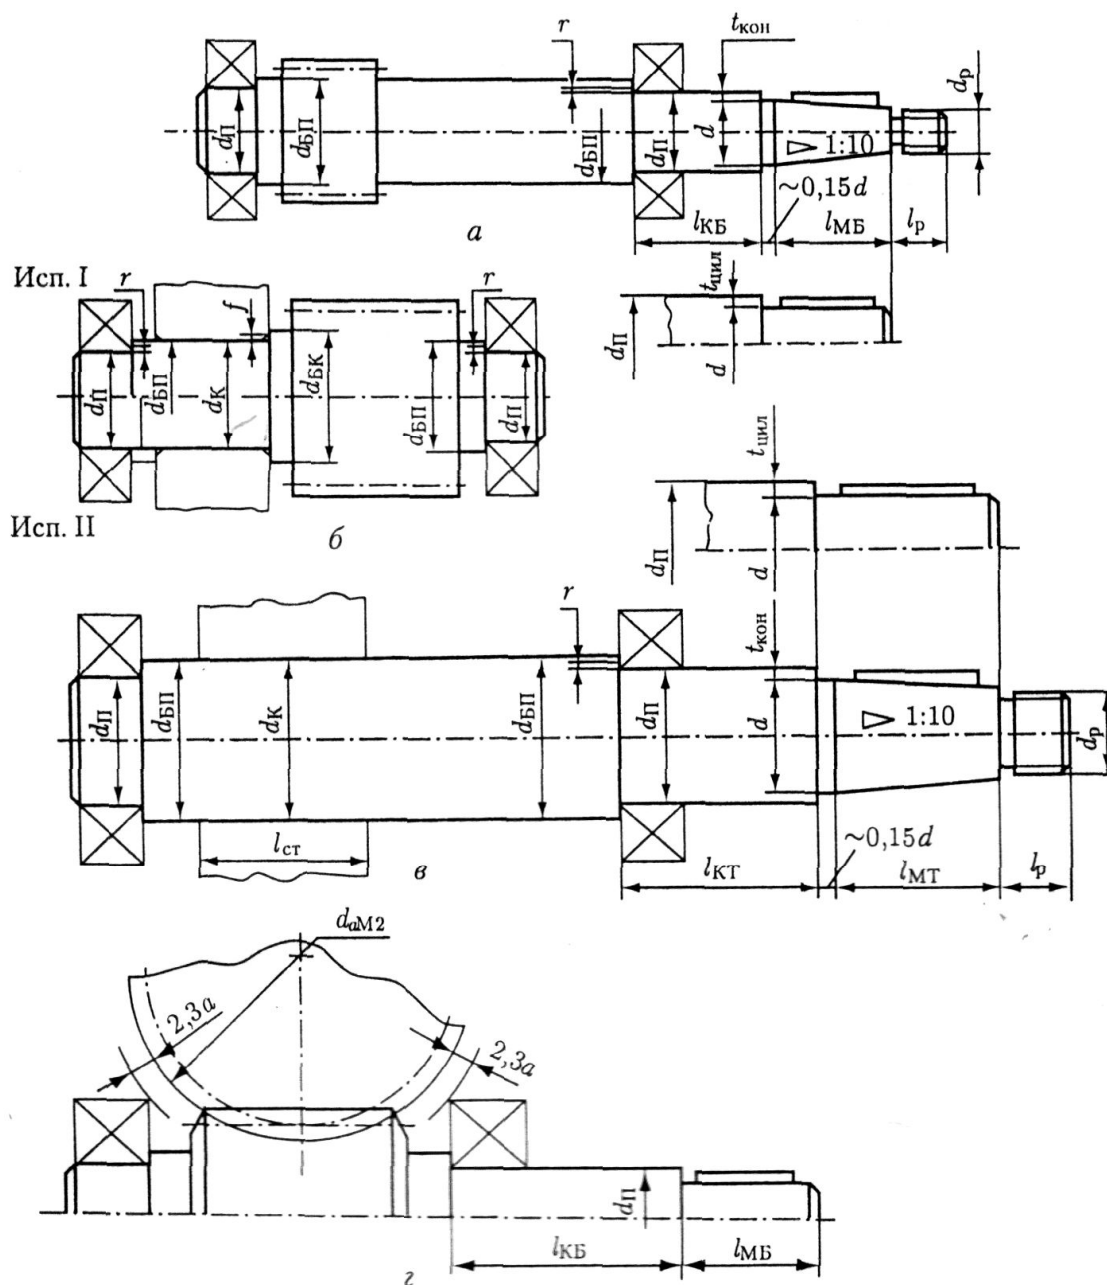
Основные размеры валов: а – быстроходный; б – промежуточный; в – тихоходный; г – червячный
